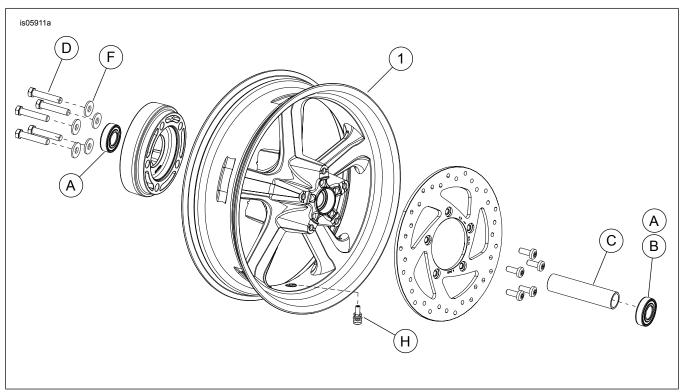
Pièces de rechange : Roue arrière en aluminium moulé à cinq rayons
